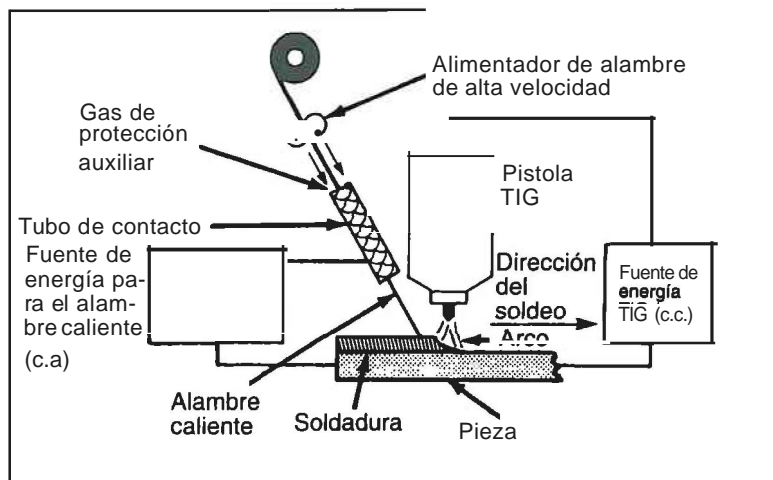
INSTALACIÓN PARA SOLDEO TIG CON ALAMBRE CALIENTE
